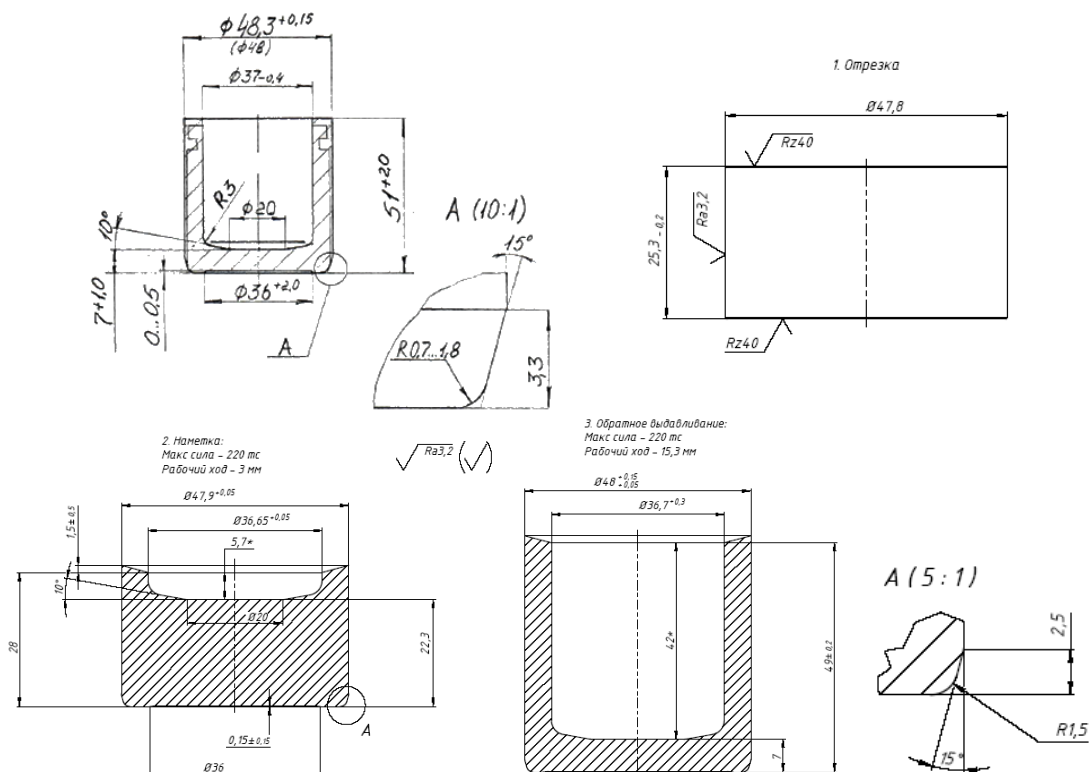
Существующий технологический процесс изготовления детали «поршень тормозного цилиндра»
